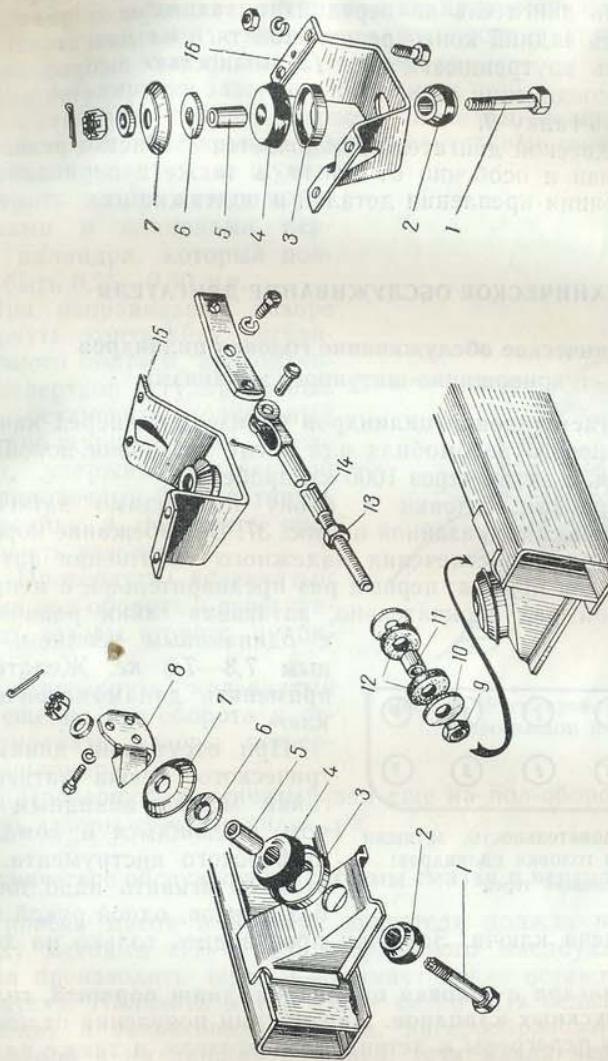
Детали подвески двигателя автомобиля УАЗ-452:
